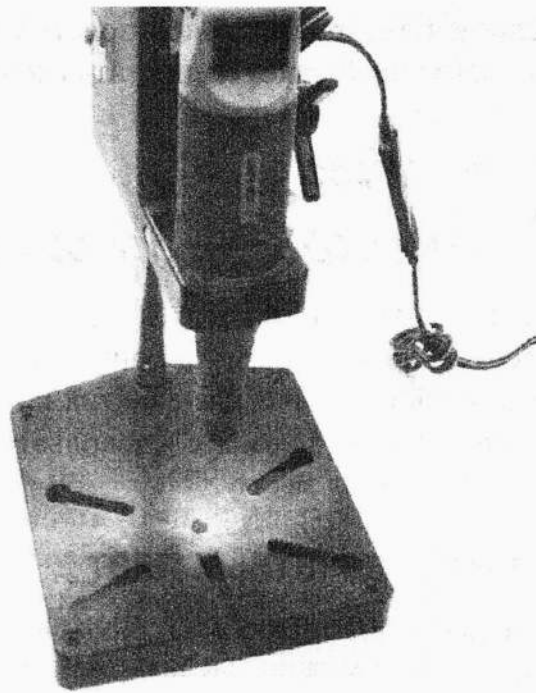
Сверлить отверстия в печатной плате значительно удобнее при помощи небольшого сверлильного станка
